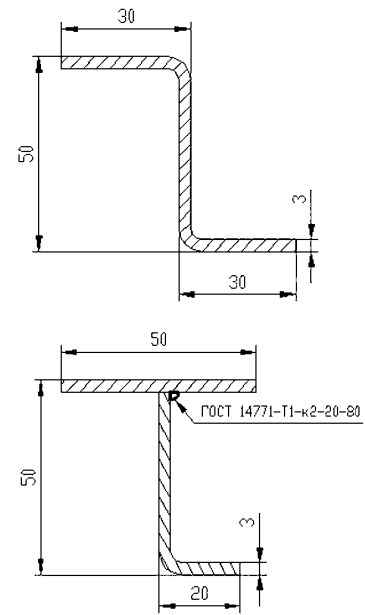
Замена Z-образного профиля на составной сварной
